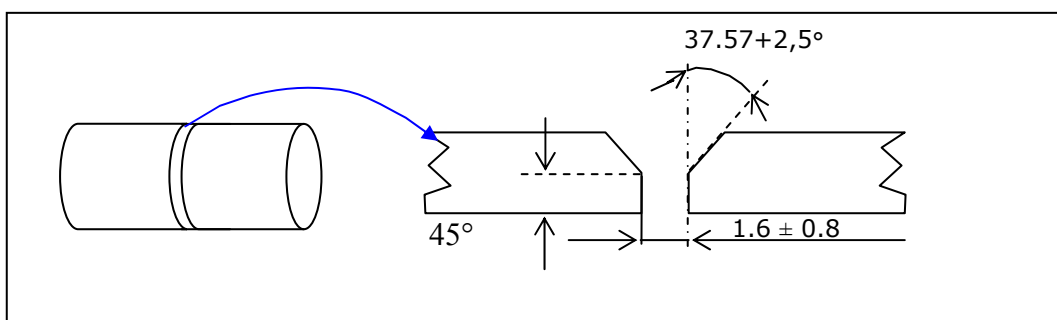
Préparation des joints en vue de soudage.
